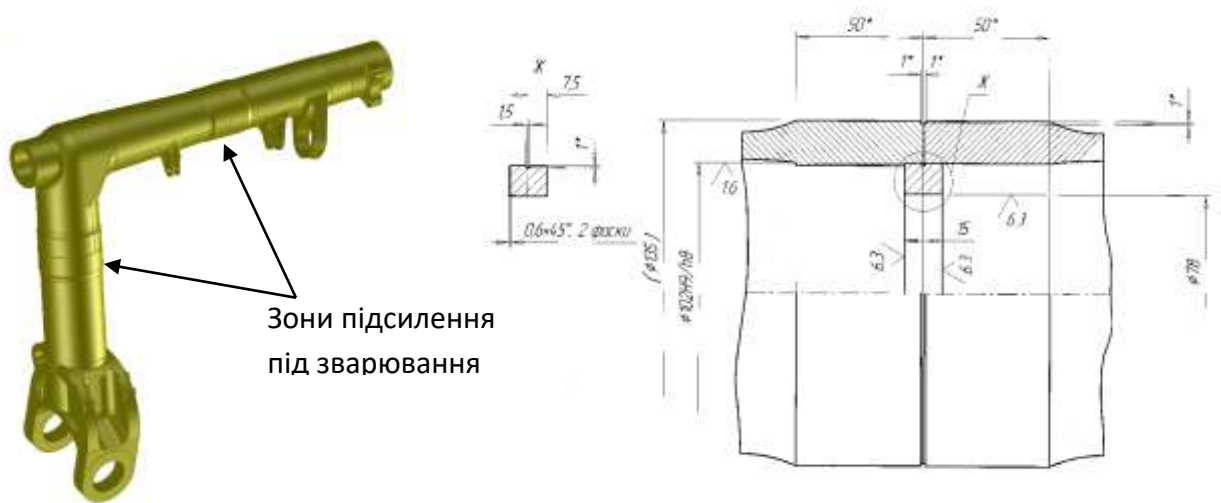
Типовий зварний вузел шасі зі сплаву VT22
